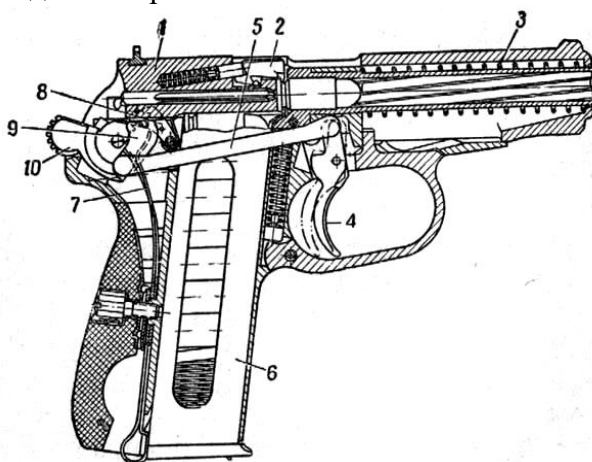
Положение частей и механизмов пистолета перед выстрелом самовзводом: 1 – затвор; 2 – выбрасыватель; 3 – возвратная пружина; 4 – спусковой крючок; 5 – спусковая тяга; 6 – магазин; 7 – боевая пружина; 8 – шептало с пружиной; 9 – рычаг взвода; 10 – курок
